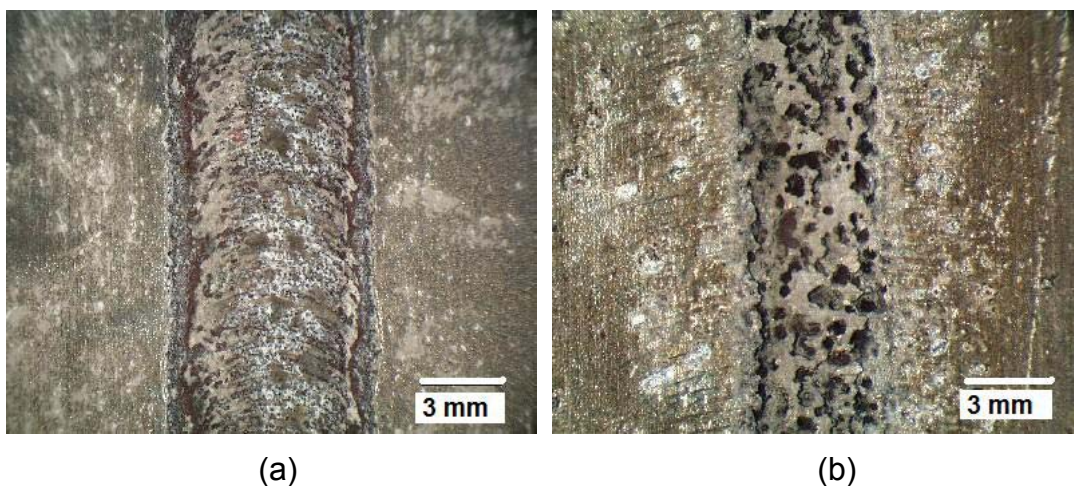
Junta soldada por FSW da liga 2024-T351 após ensaio de corrosão intergranular; (a) face da solda e (b) raiz da solda.
